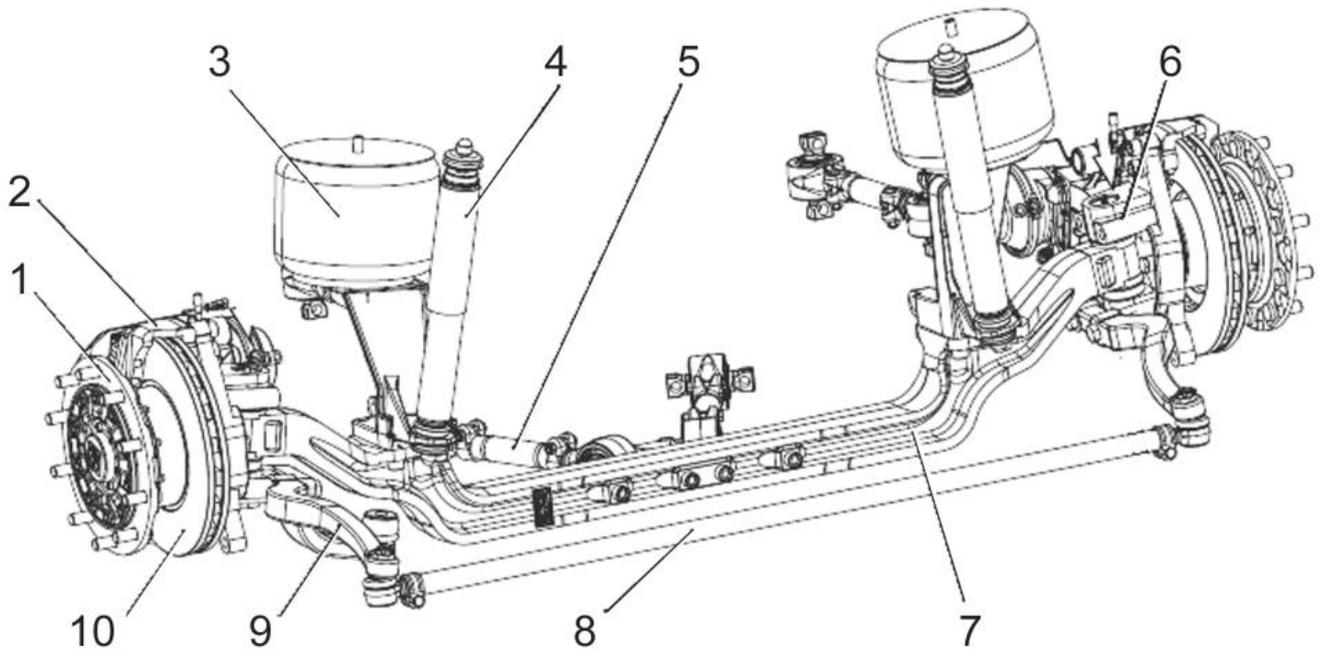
Передняя ось с реактивными штангами и пневмобаллонами подвески
